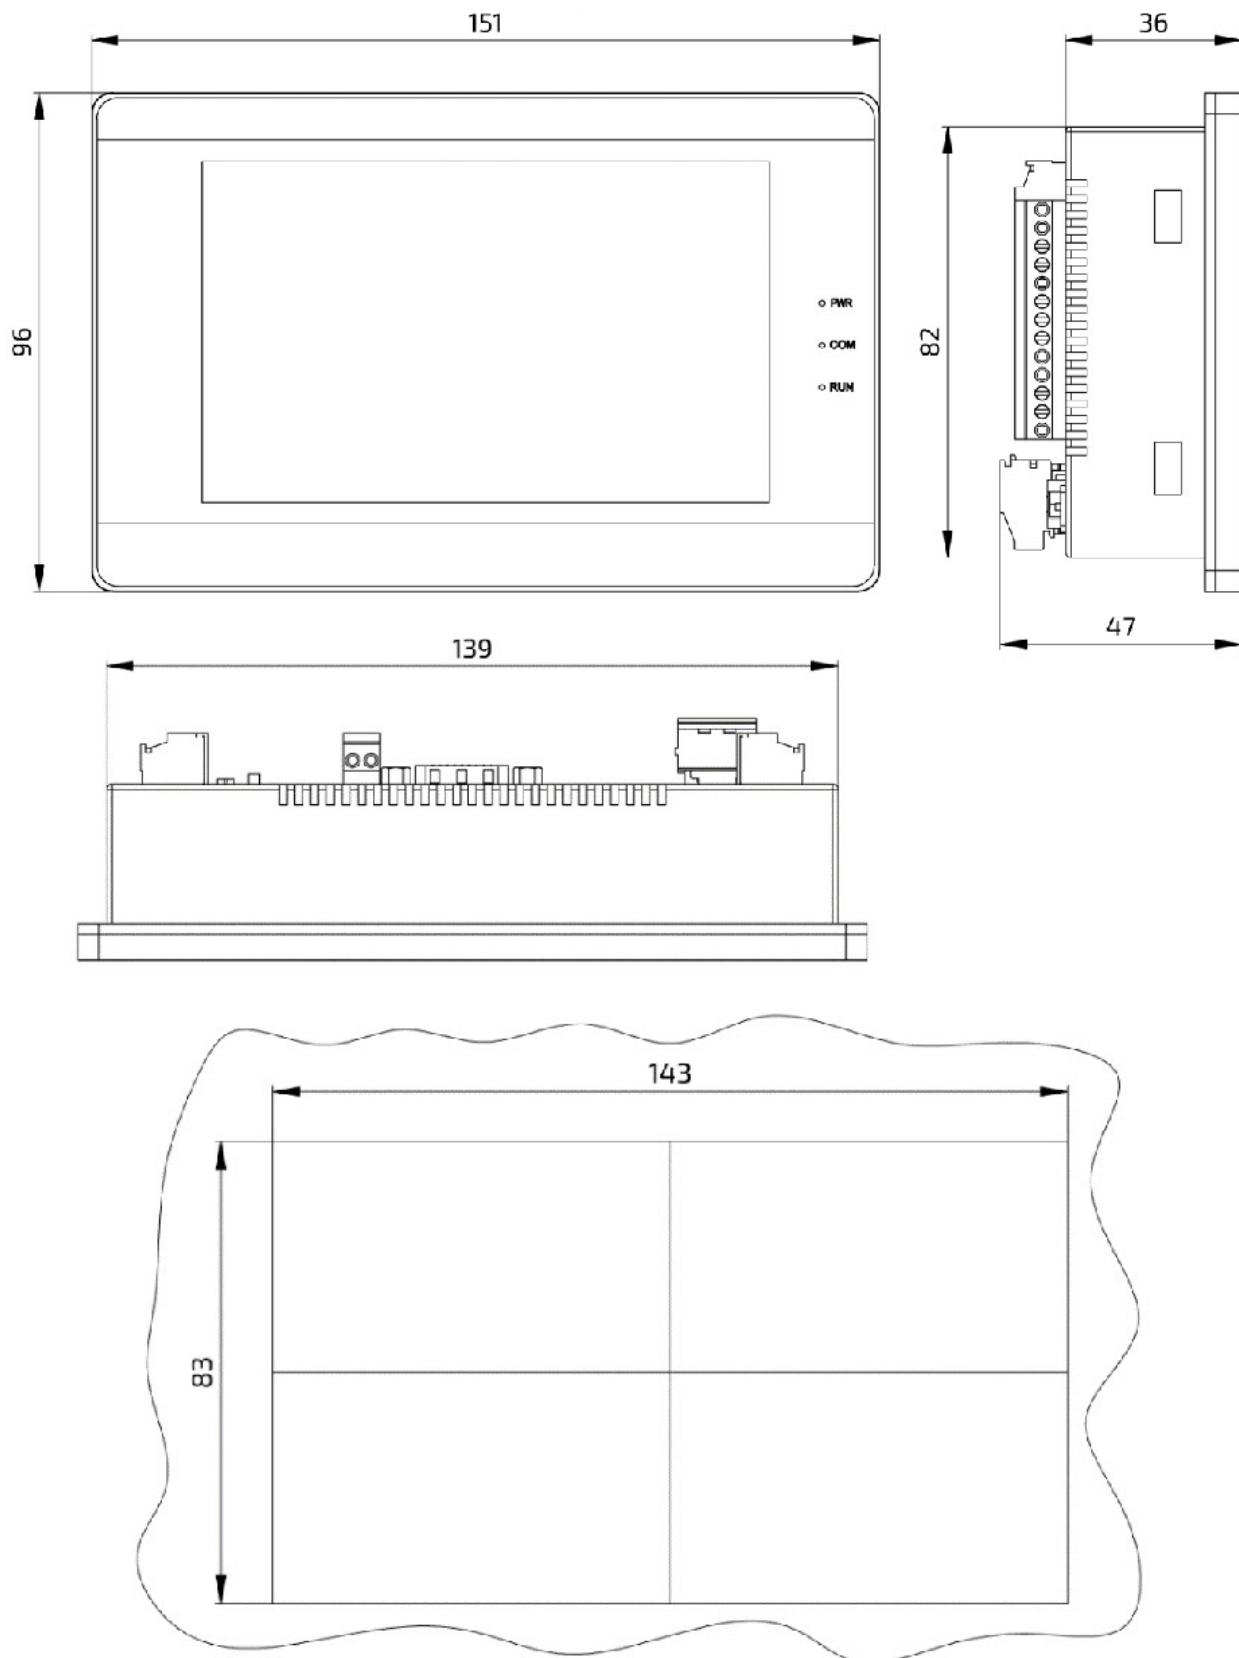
Габаритные и установочные размеры Смарт АВР (мм)
